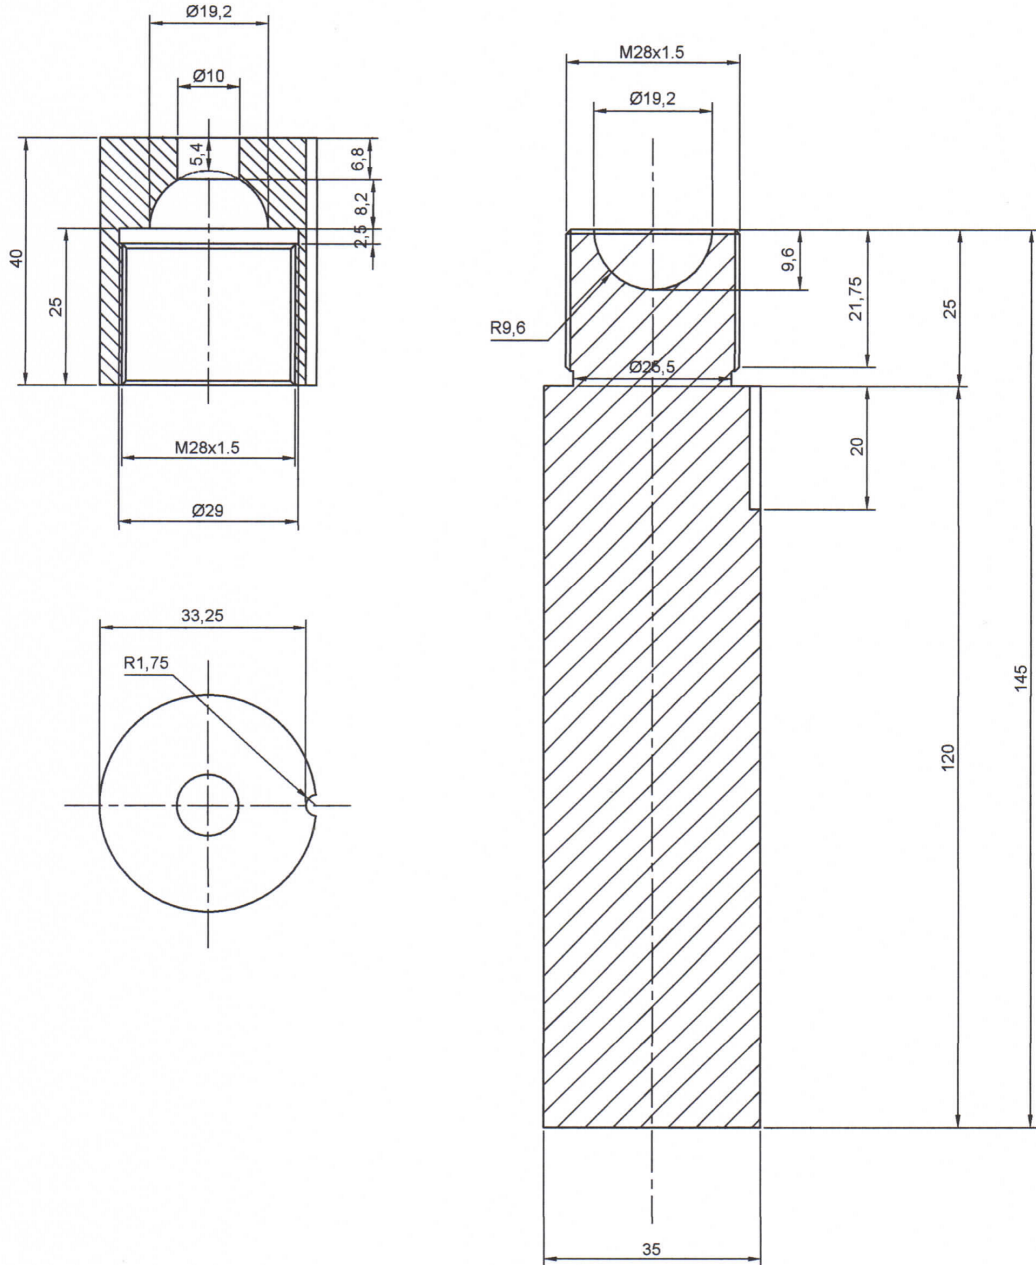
Desenho técnico- Black Body Insert( Corpo negro)
